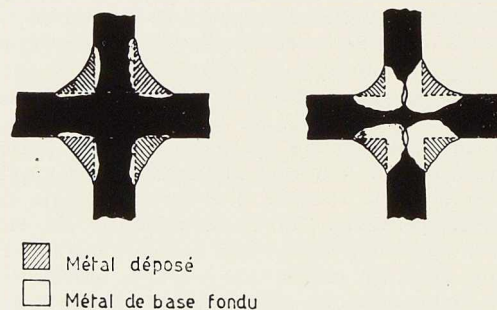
Soudure d'angle. La technique de la forte pénétration diminue la quantité de métal à déposer et conduit à un assemblage de haute qualité notamment en ce qui concerne la limite d'endurance. A gauche : technique courante. A droite : technique de la forte pénétration.
